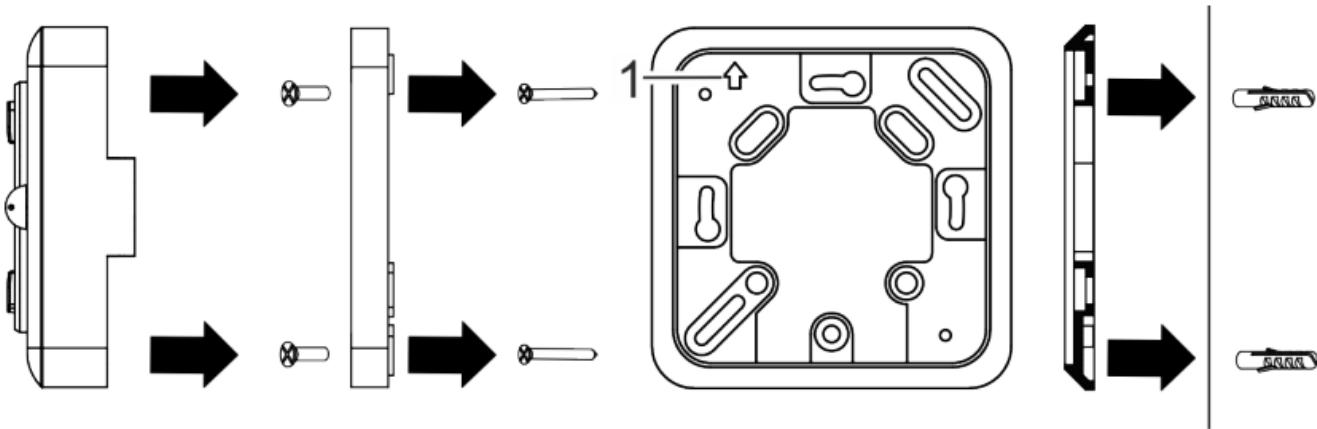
Montar el fondo de la carcasa sobre la placa de montaje
